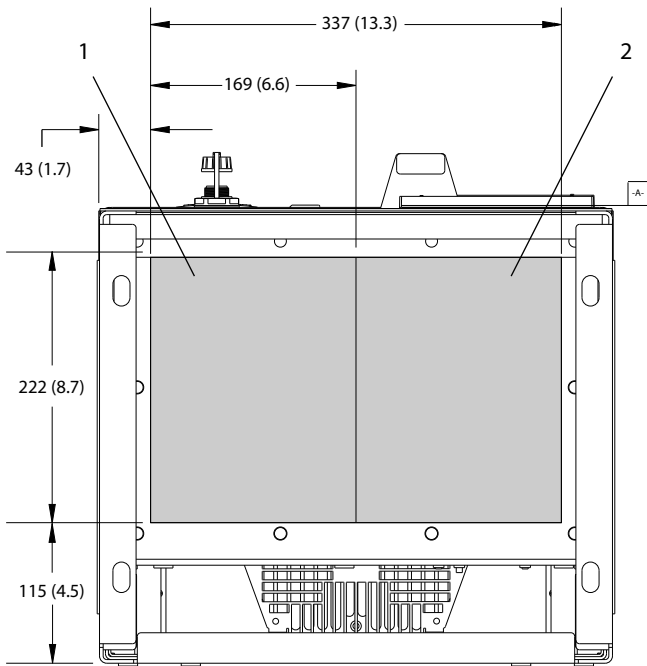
Dimensi Dudukan Dinding untuk D7h
